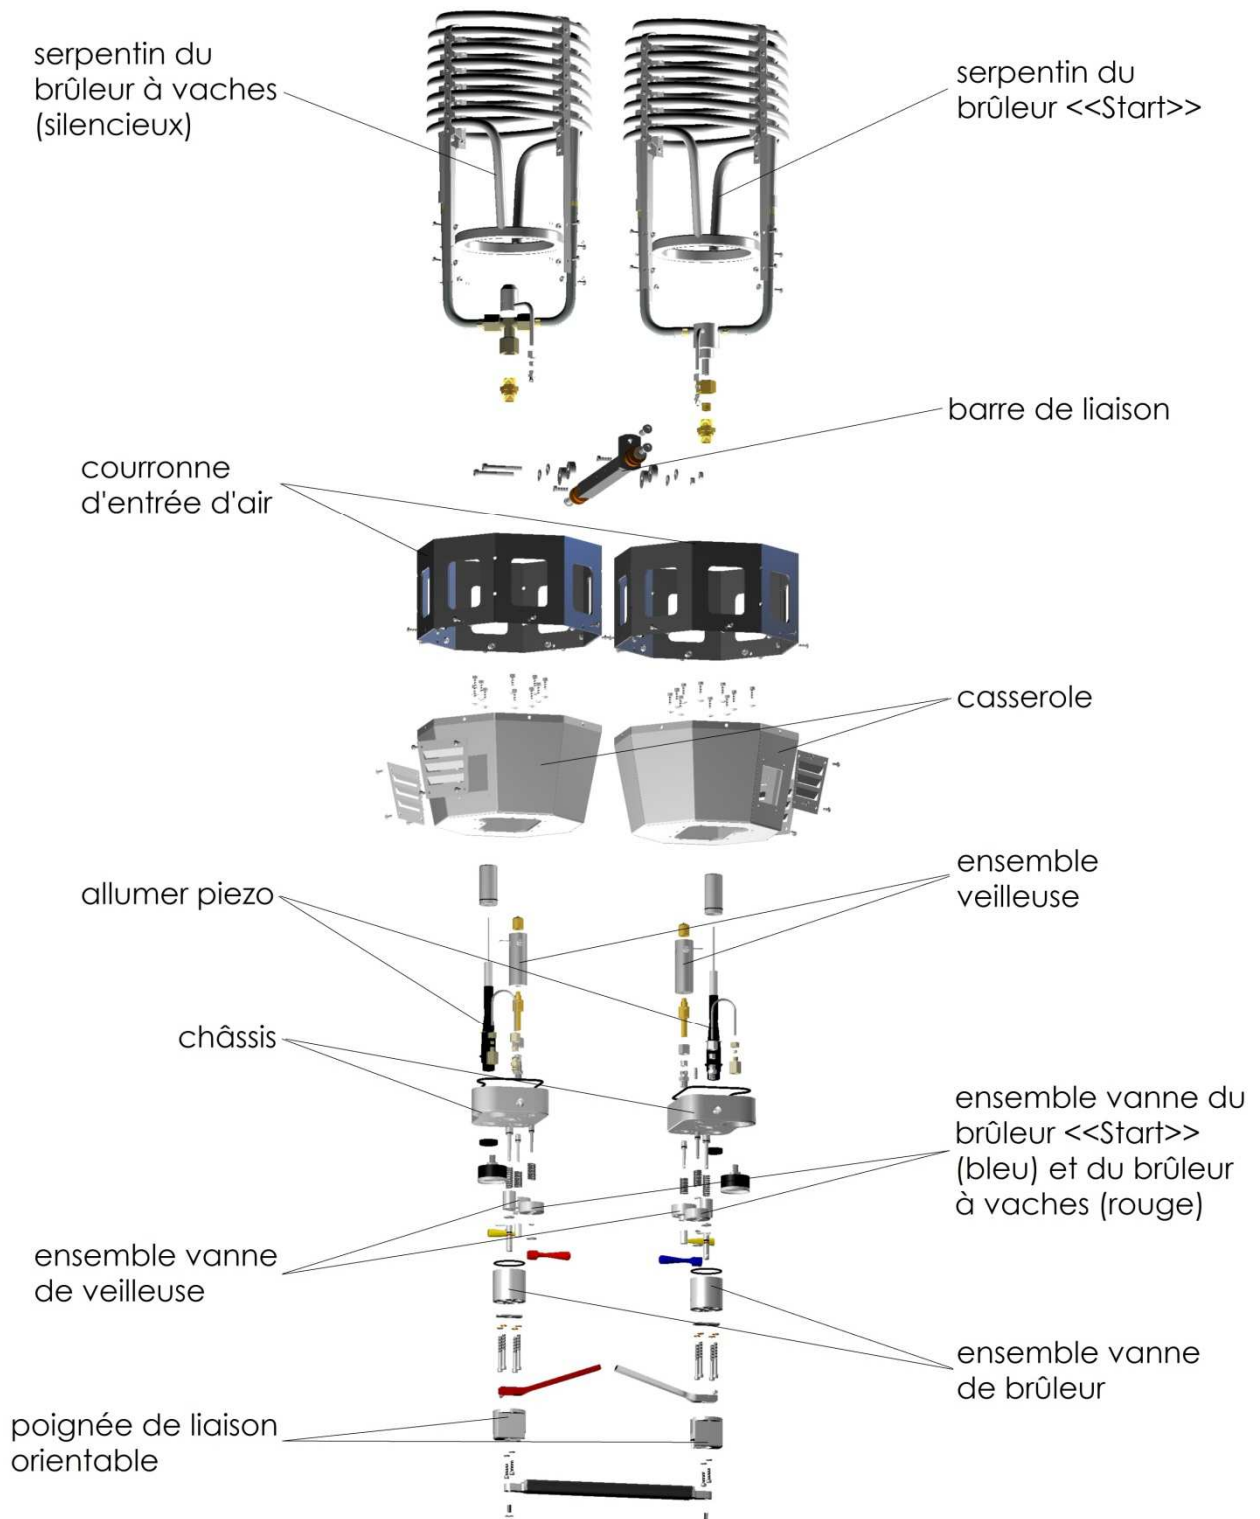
Vue éclatée de l'assemblage du brûleur FB6
